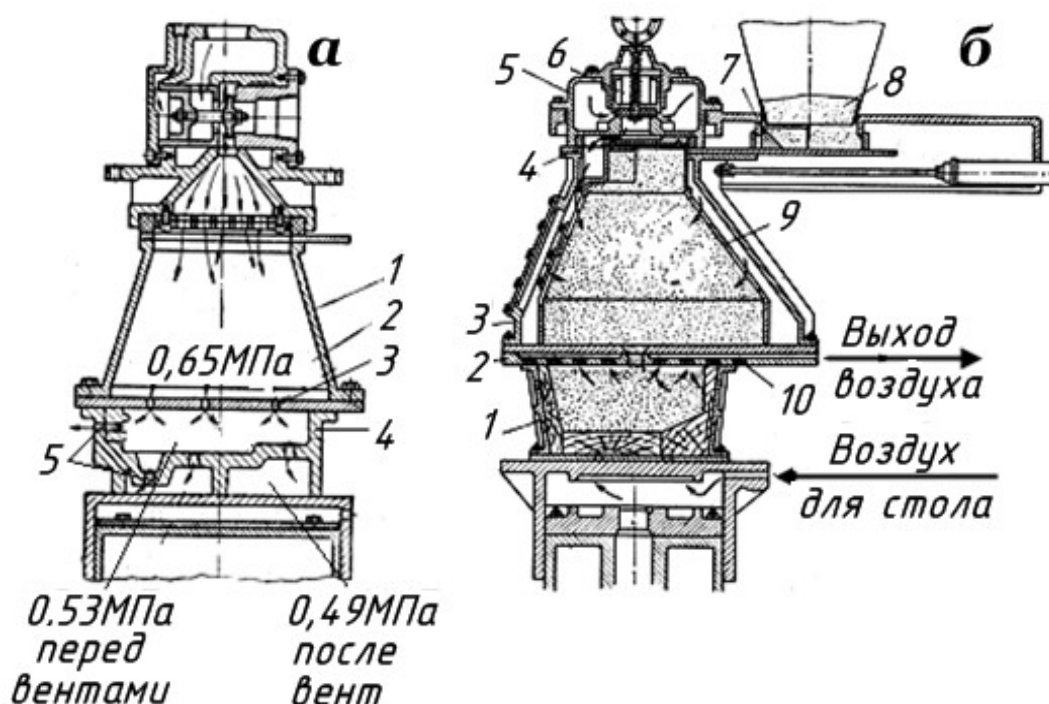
Пескодувная машина 287: а – схема пескодувной стержневой установки; б – общий вид пескодувной машины: 1 – металлический ящик; 2 – вдувная плита; 3 – резервуар; 4 – вдувное кольцо; 5 – воздушная коробка; 6 – клапан; 7 – полукольцо; 8 – бункер; 9 – внутренний резервуар со щелевыми прорезами; 10 – вен-
